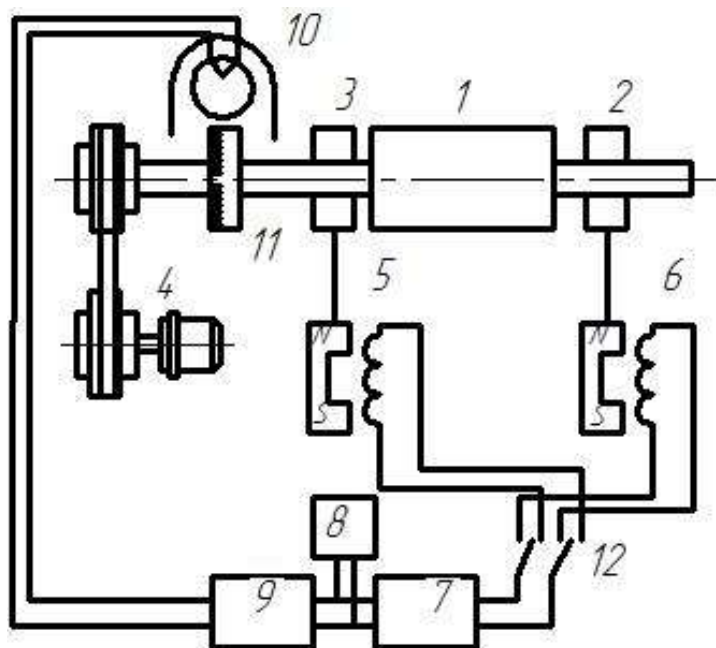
Принципова схема верстата для динамічного балансування
